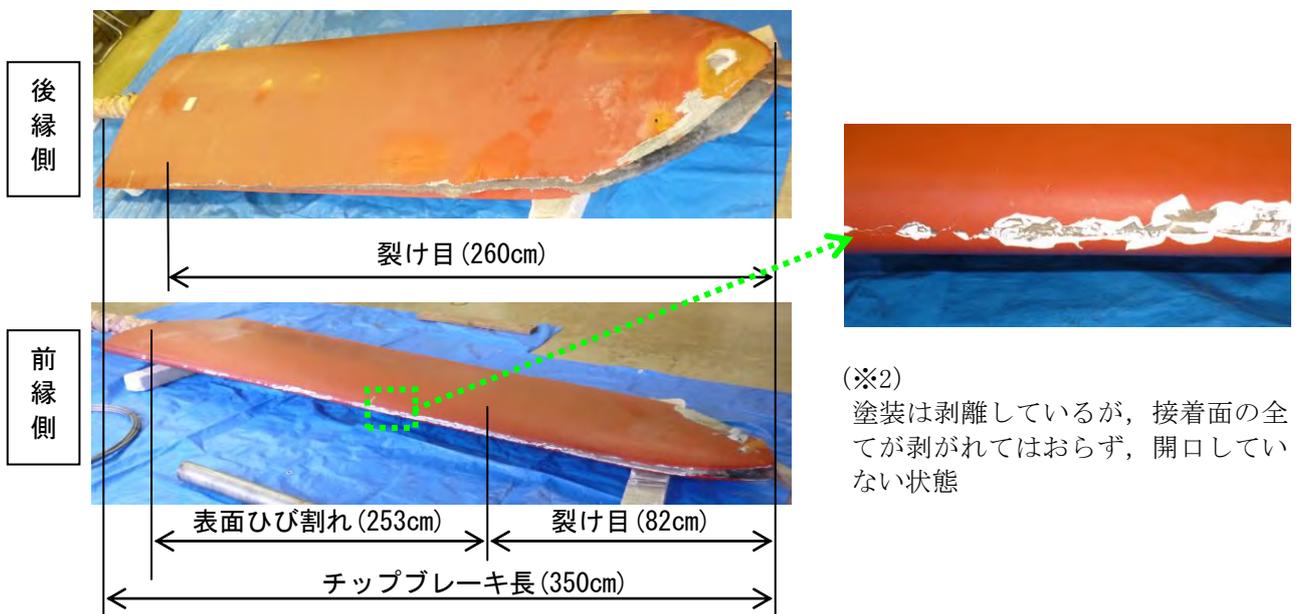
チップブレーキの裂け目および表面ひび割れ状況
